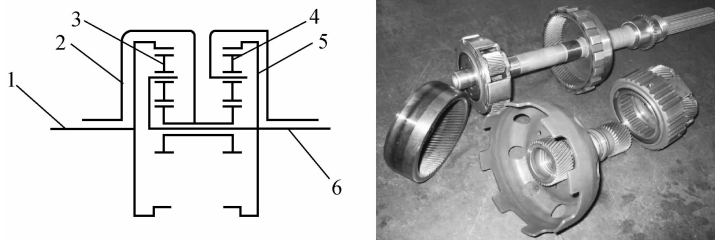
三挡辛普森式双排行星齿轮机构组合传动简图
